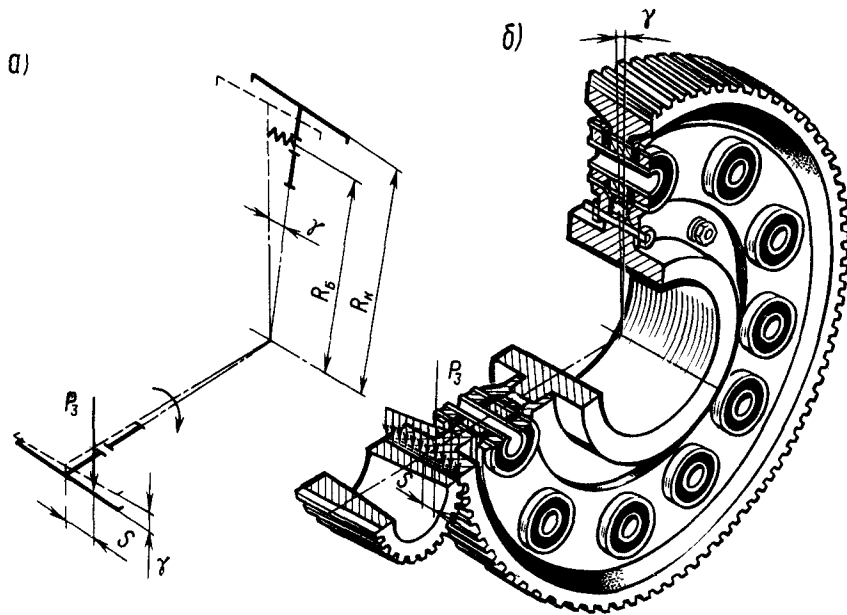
Схема самоустановки упругого зубчатого венца в плоскость вращения шестерни двигателя
